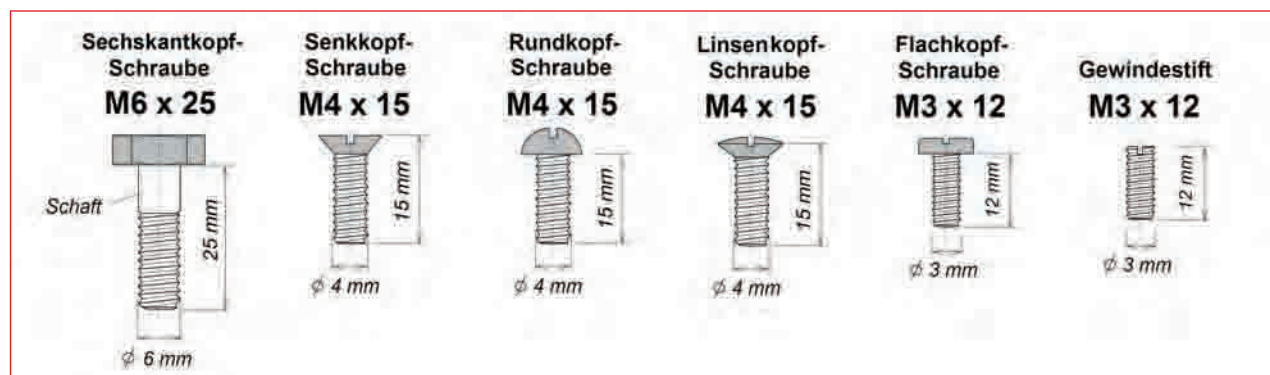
Übersicht der gängigsten Schraubenschlitze (Gewindestifte, die auch als „Madenschrauben“ bezeichnet werden, haben allerdings keinen Kopf).
